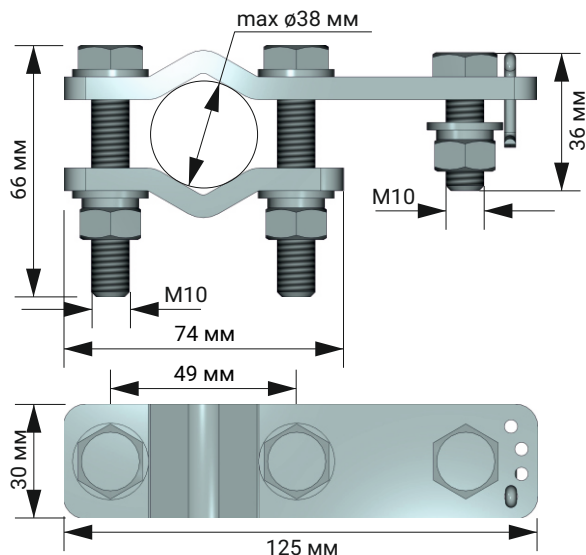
Габаритные и присоединительные размеры кронштейна
